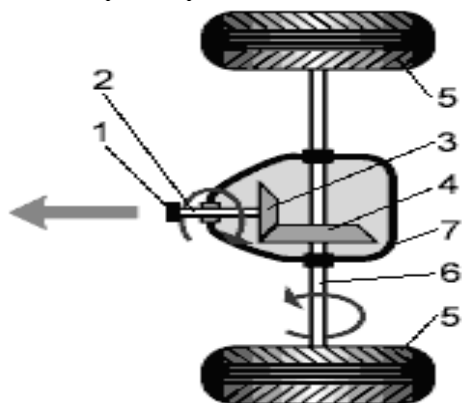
Схема работы главной передачи 1 - фланец; 2 - вал ведущей шестерни; 3 - ведущая шестерня; 4 - ведомая шестерня; 5 - ведущие (задние) колеса; 6 - полуоси; 7 - картер главной передачи
